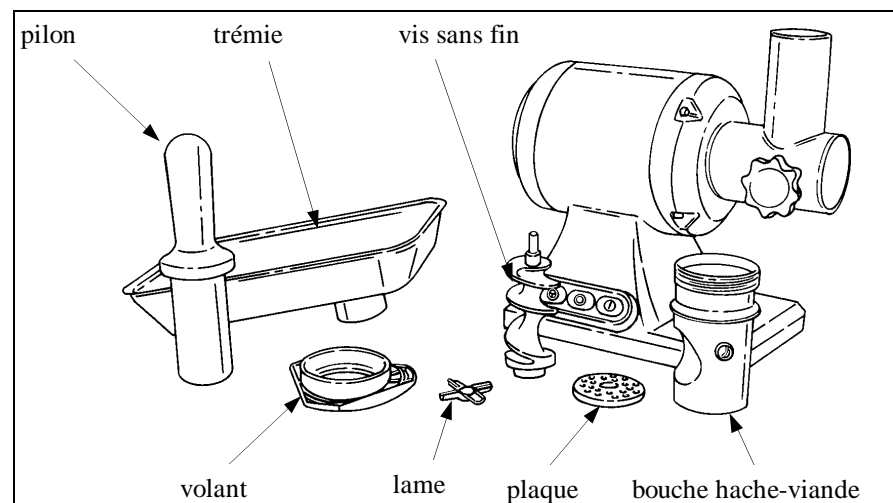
Vue du TC désassemblé pour le nettoyage
